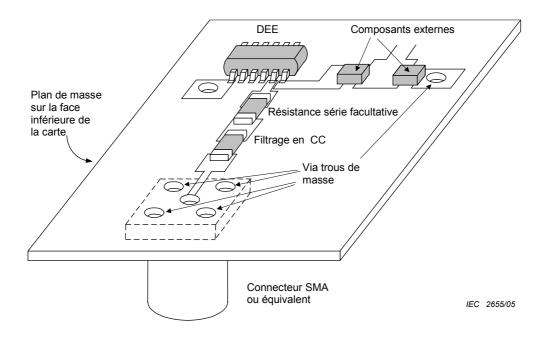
Installation d'un connecteur sur la carte d'essai à proximité du DEE
